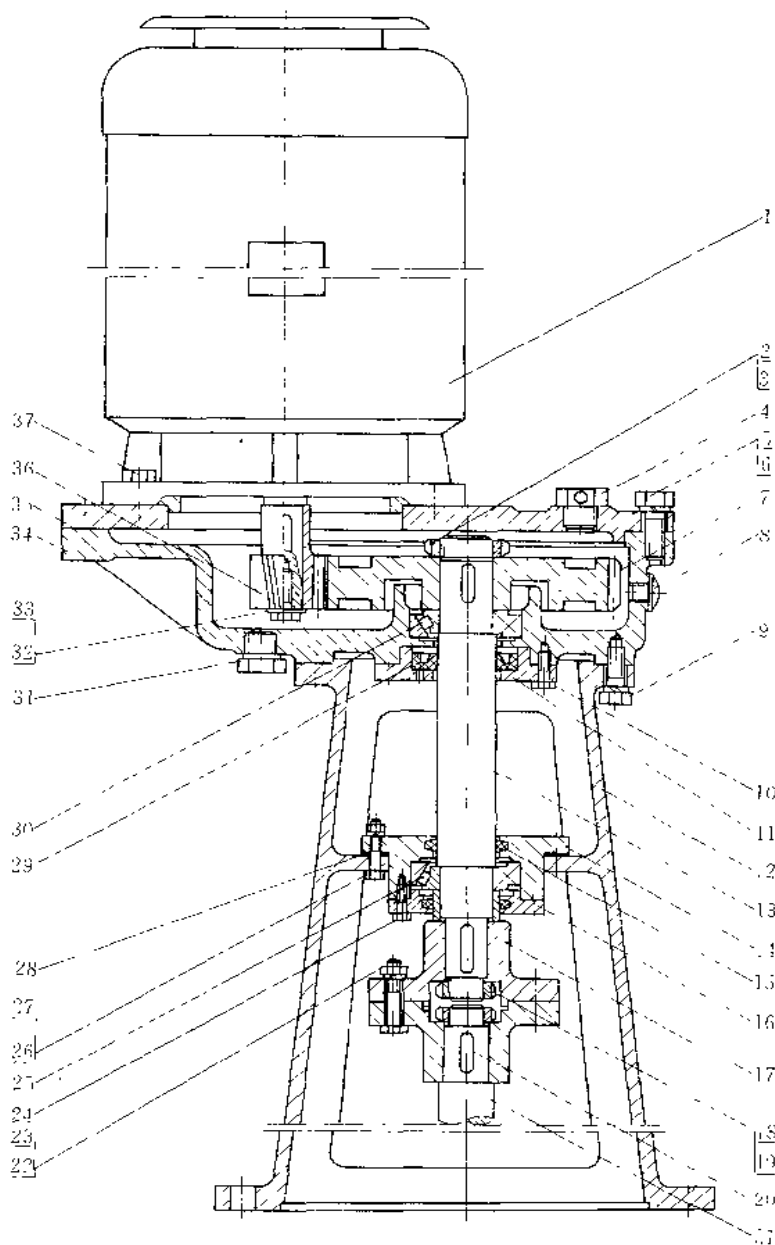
DJC 型立式单级圆柱齿轮减速器
